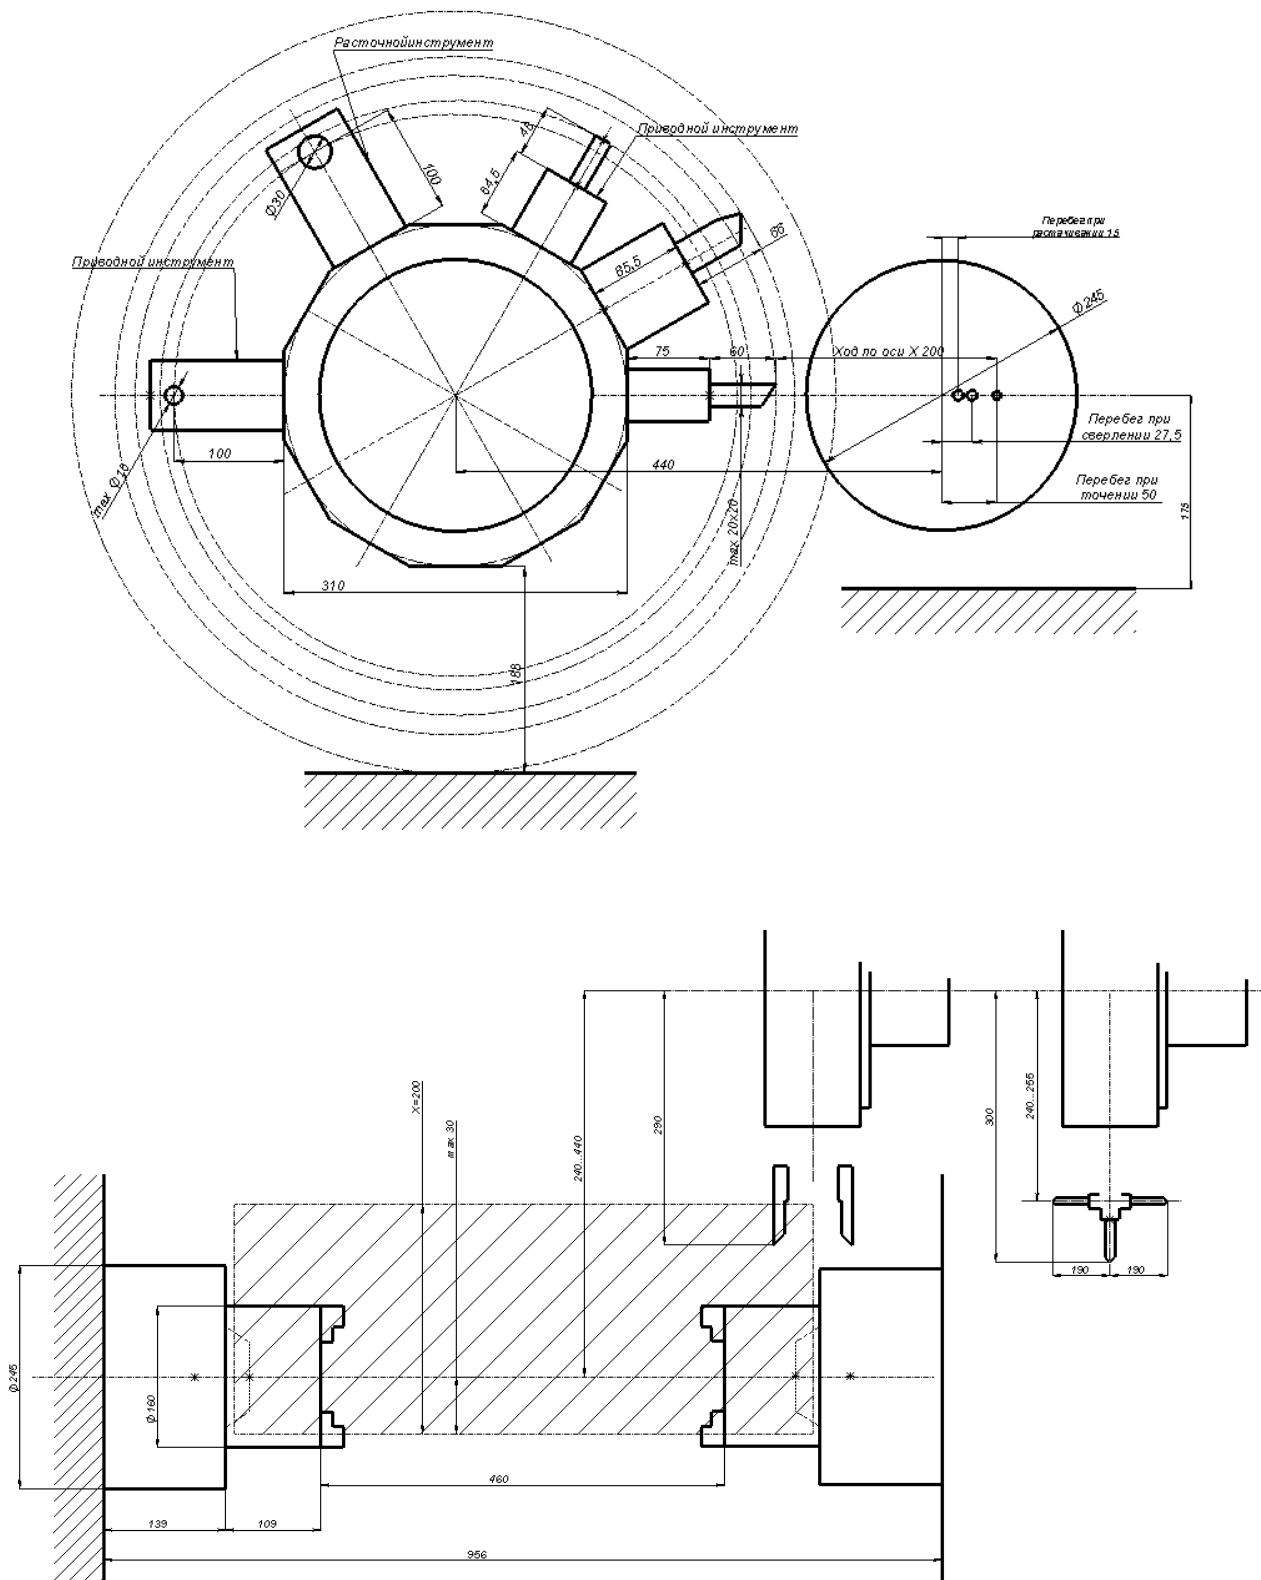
Зона резания токарного обрабатывающего центра с ЧПУ модели «ТМ-160»
